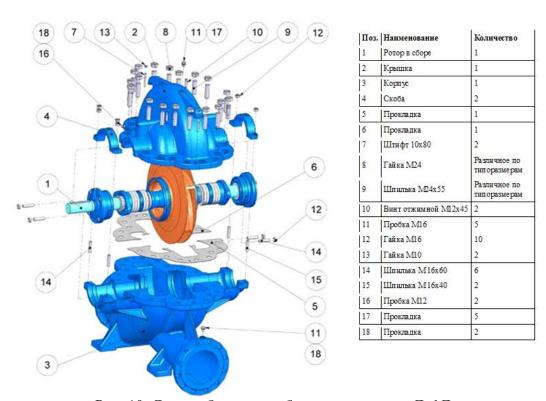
Схема сборки и разборки насоса типа Д, 1Д
